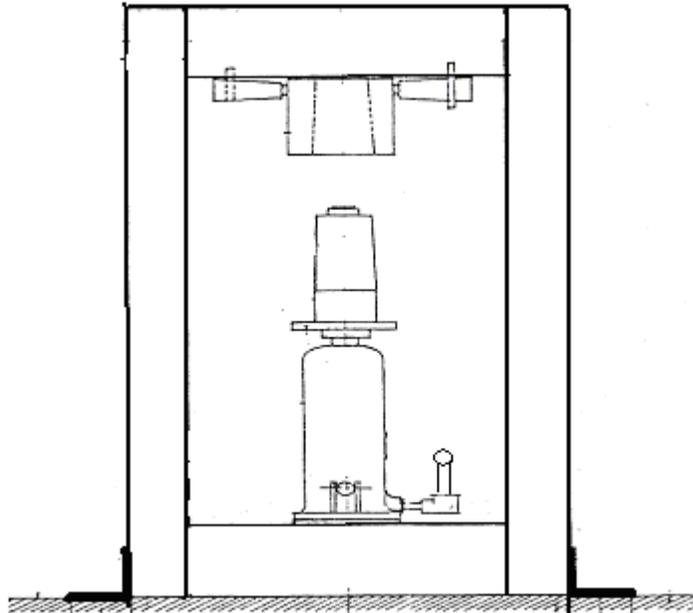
Soporte en “Rectángulo” con sus principales elementos
